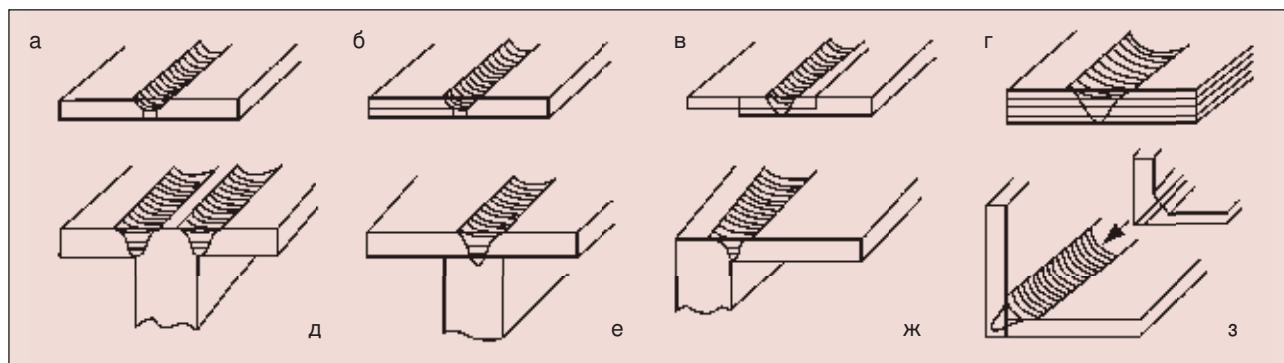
Основные типы соединений, выполняемые сваркой трением с перемешиванием: а – стыковое; б – нахлесточно-стыковое; в – нахлесточное; г – многослойное нахлесточное; д – двухпроходное тавровое; е – тавровое прорезное; ж, з – угловое
